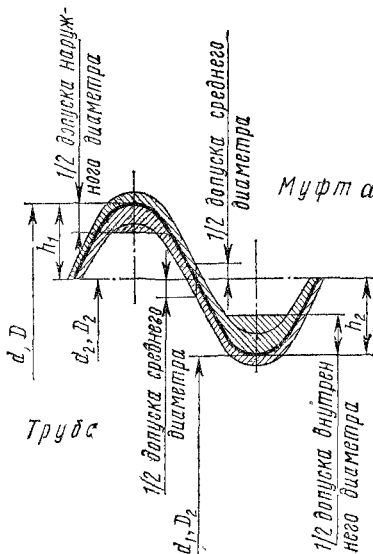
Схема расположения полей допусков трубной цилиндрической резьбы:
